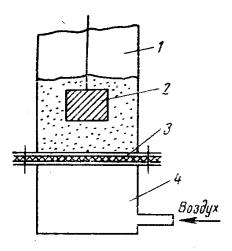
Схема одноместной установки нанесения полимерного покрытия: 1 – камера рабочая; 2 – изделие; 3 – перегородка пористая; 4 – камера воздушная
